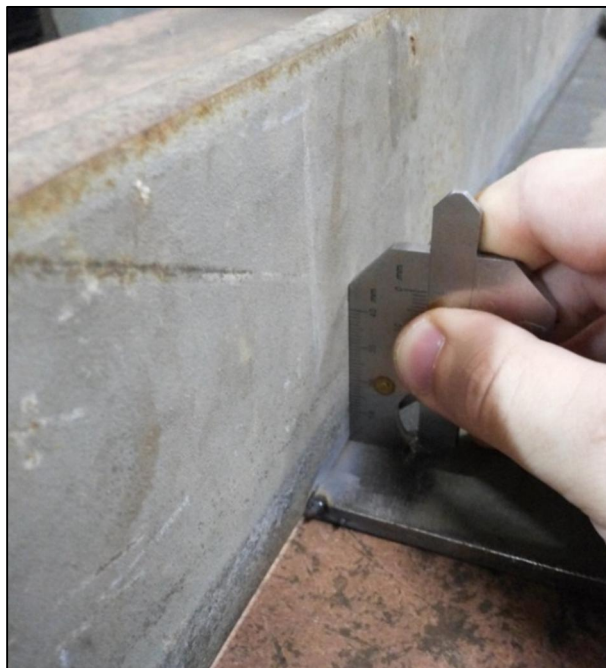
Dimensões dos corpos-de-prova - ângulo reto.
